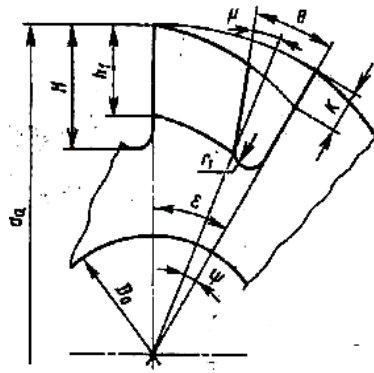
Конструктивные элементы затылованного зуба фрезы:
